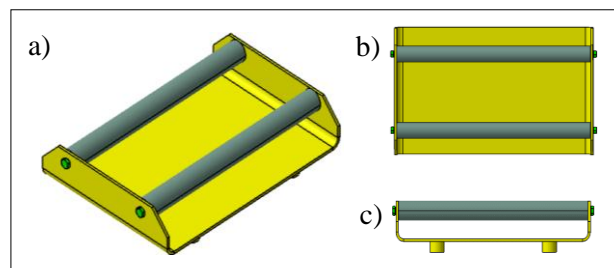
Kit Modular Rolagem: a) Vista isométrica; b) Vista superior; c) Vista lateral.
